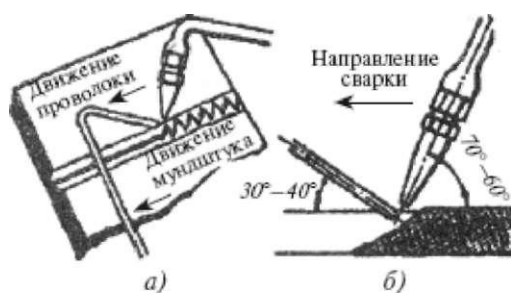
Левая сварка: а - схема движений мунштука и горелки; б - углы наклона мунштука и проволоки
